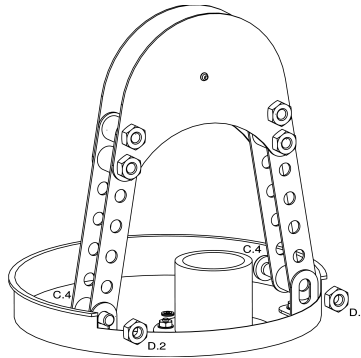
Verbindung Lageraufbau - Gehäusedeckel
